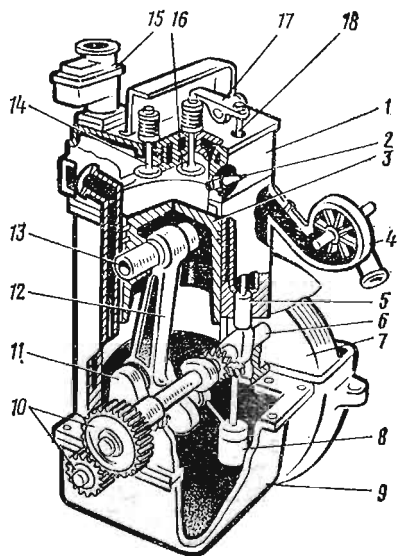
Одноцилиндровый карбюраторный двигатель:
